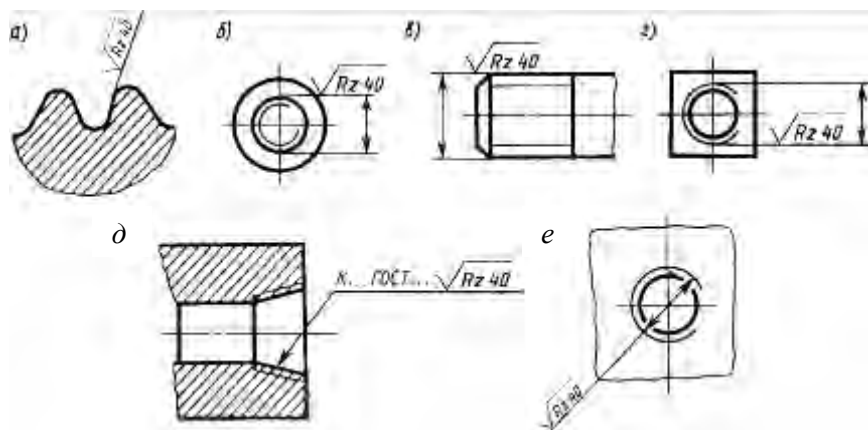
Обозначение шероховатости поверхности профиля резьбы
